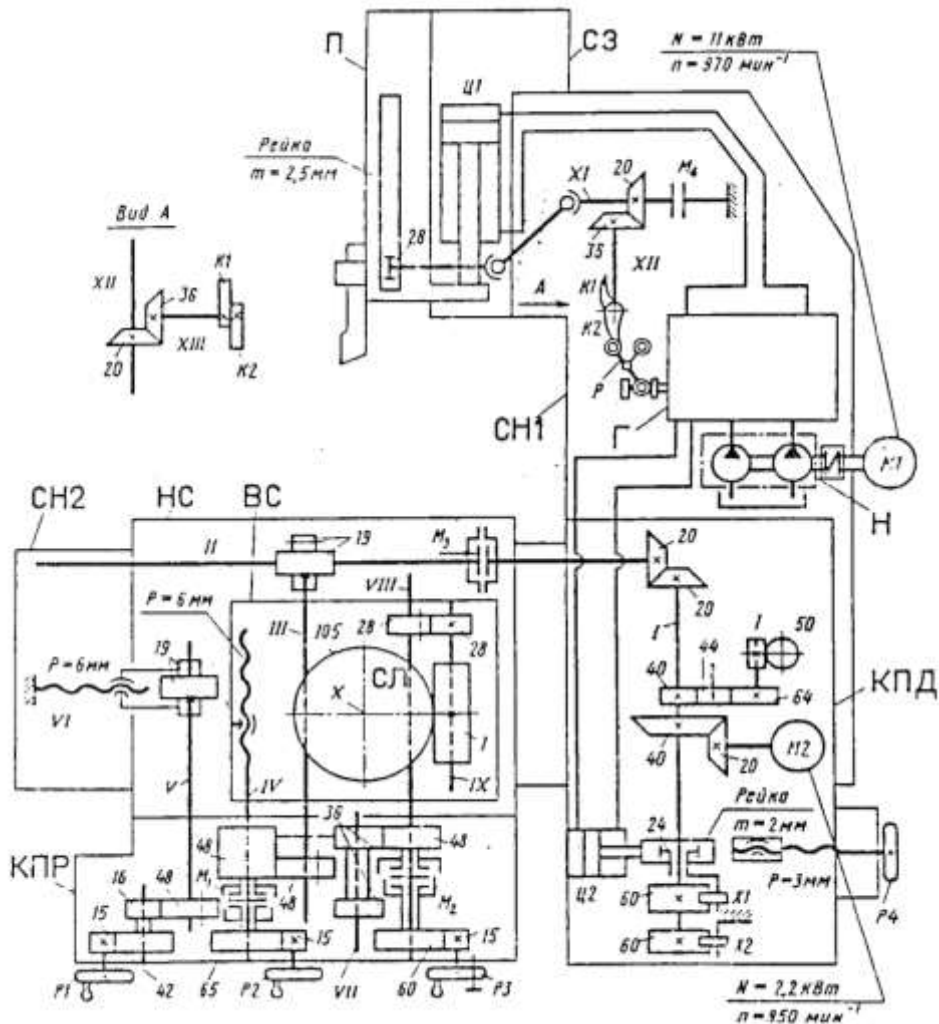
Кинематическая схема долбежного станка 7Д430
